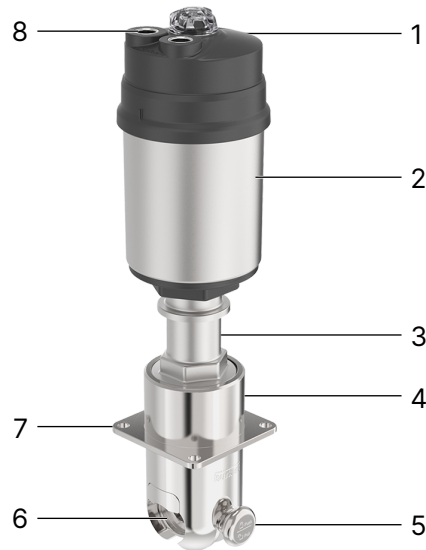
Aufbau des Schlauchquetschventils, ELEMENT-Variante, Beispiel
